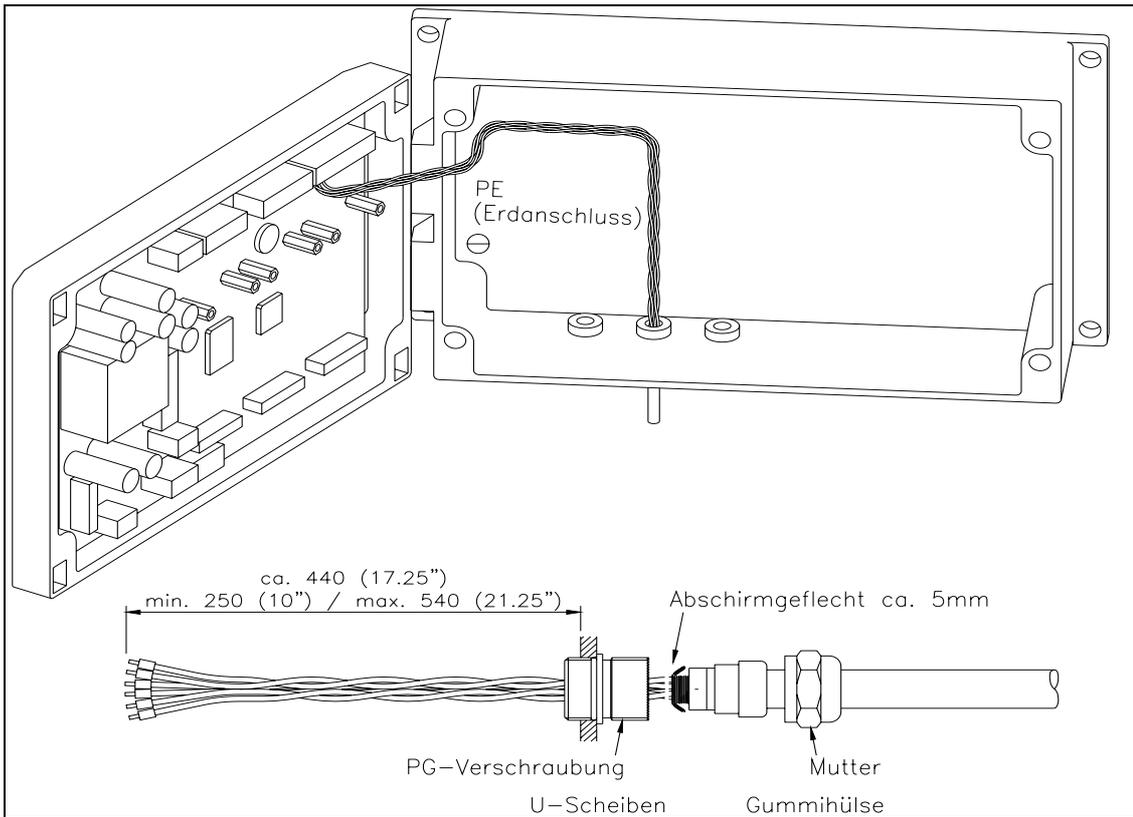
Verlauf der Anschlusskabel im Gehäuse
